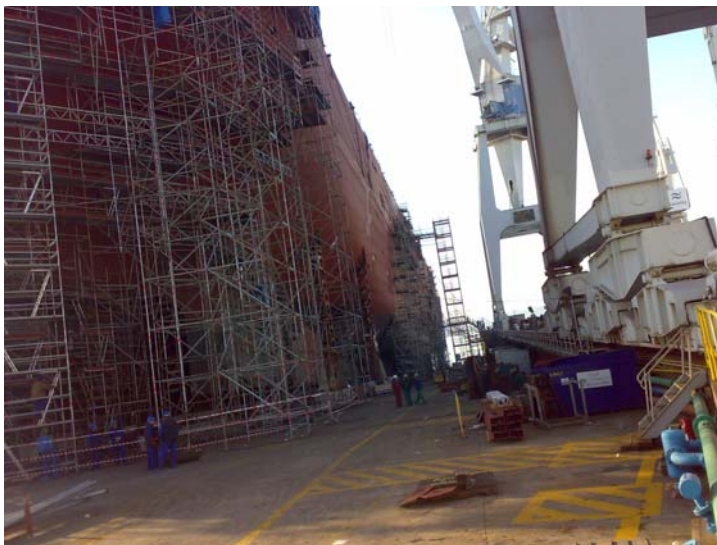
Imagen de la construcción del buque Juan Carlos I. Se trata de un sistema robotizable de producción de piezas con series cortas. En la industria naval se emplean células de soldadura por arco para crear módulos, que luego se unen en el astillero. (Robots en sistema gantry con corinas de protección)
